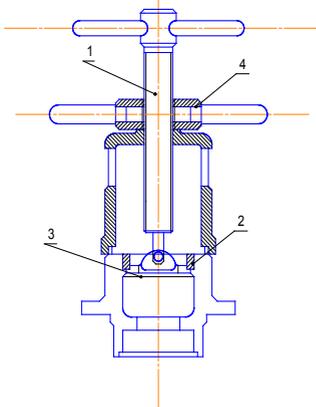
Съемник для выпрессовки подшипников из ступицы колеса с помощью упора
